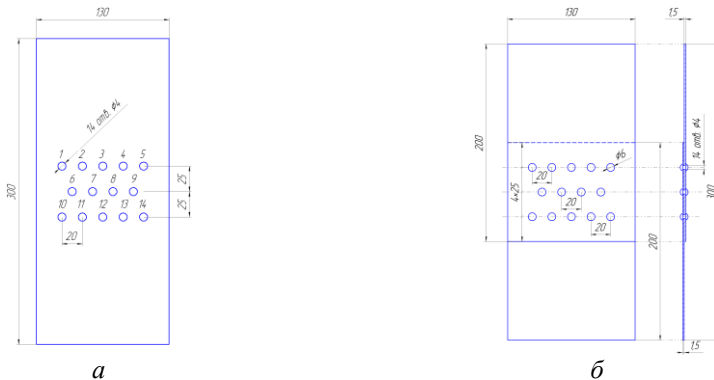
Зразки для випробувань: а – суцільний зразок з отворами під заклепку; б – заклепкове з'єднання, яке моделює фрагмент обшивки ЛА
